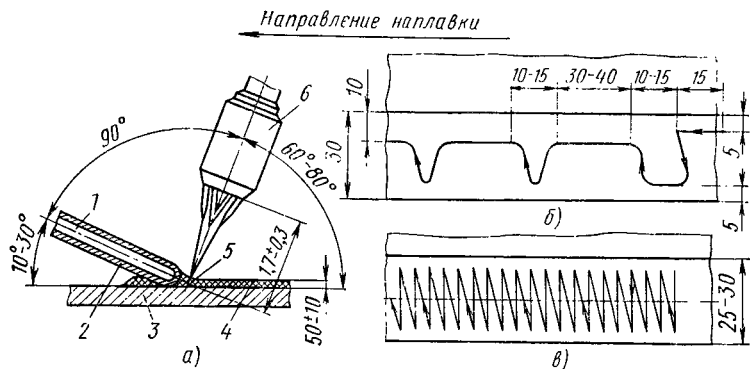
Положение и движение горелки и присадочного прутка при наплавке:
